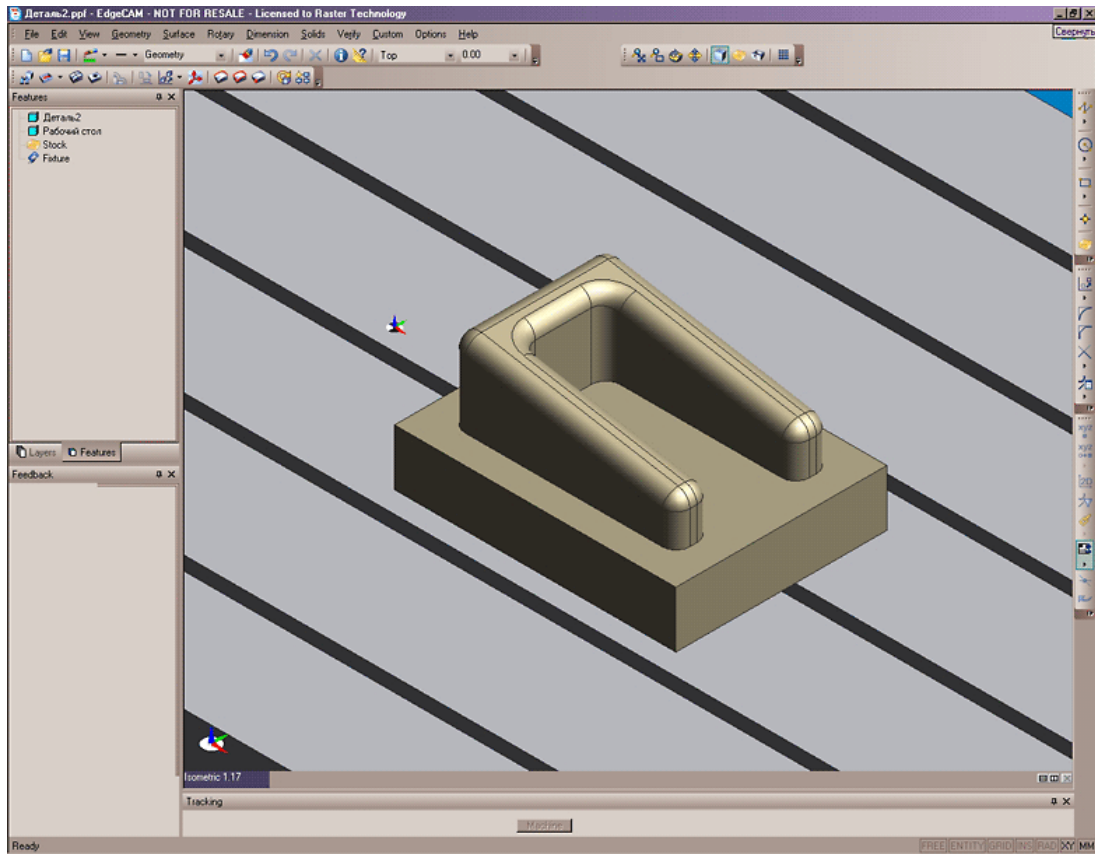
Модель детали полученной в Autodesk Inventor и загруженной в Edgcam
